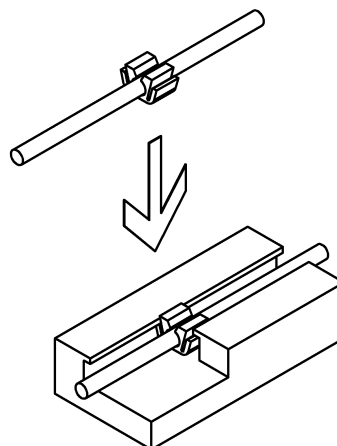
Clip de cable para cables con $\varnothing 2,4 \text{ mm}$
